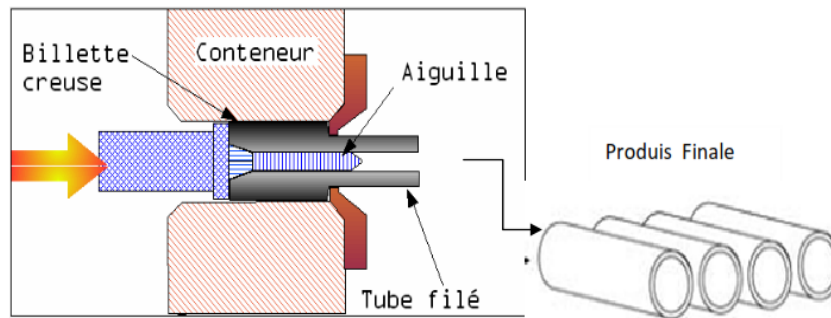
Fabrication de pipeline sans soudure.
